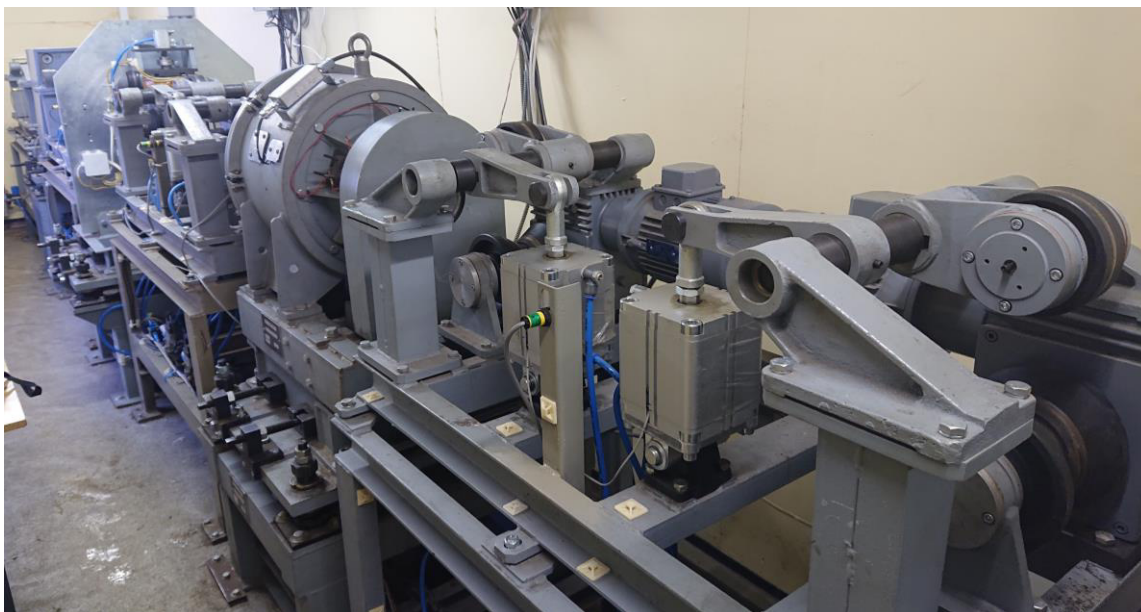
Общий вид установок неразрушающего контроля насосно-компрессорных труб
